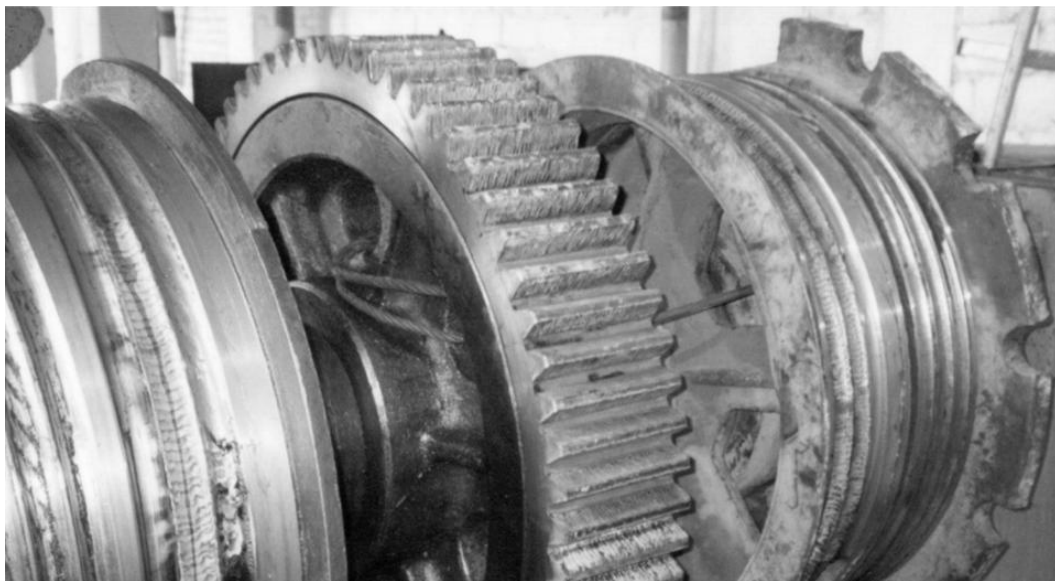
Канатные барабаны и приводная шестерня редуктора «напора» экскаватора ЭКГ-8А, упрочненные плазменной закалкой
